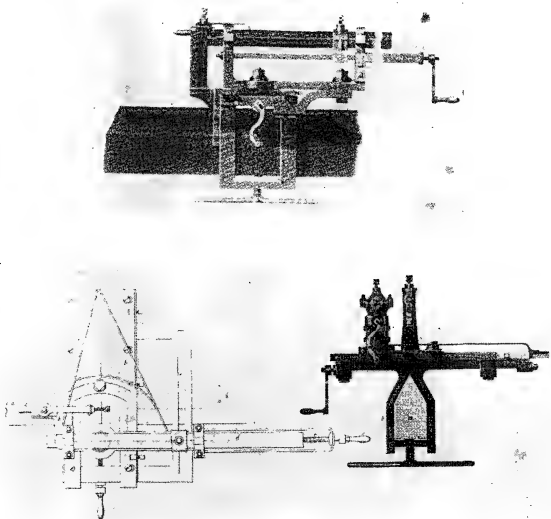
Первый суппорт токарного станка, изготовленный Г. Модсли. 1794 г. По Дж. Реппи.
